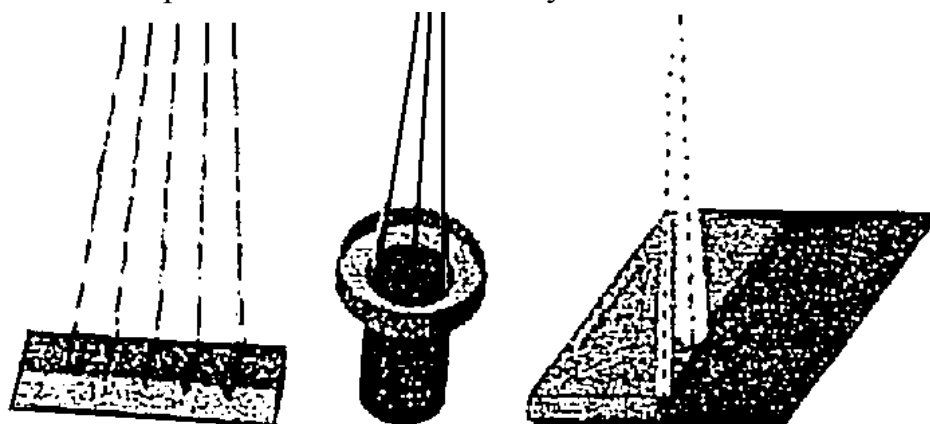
Электронно-лучевая сварка с параллельными швами
